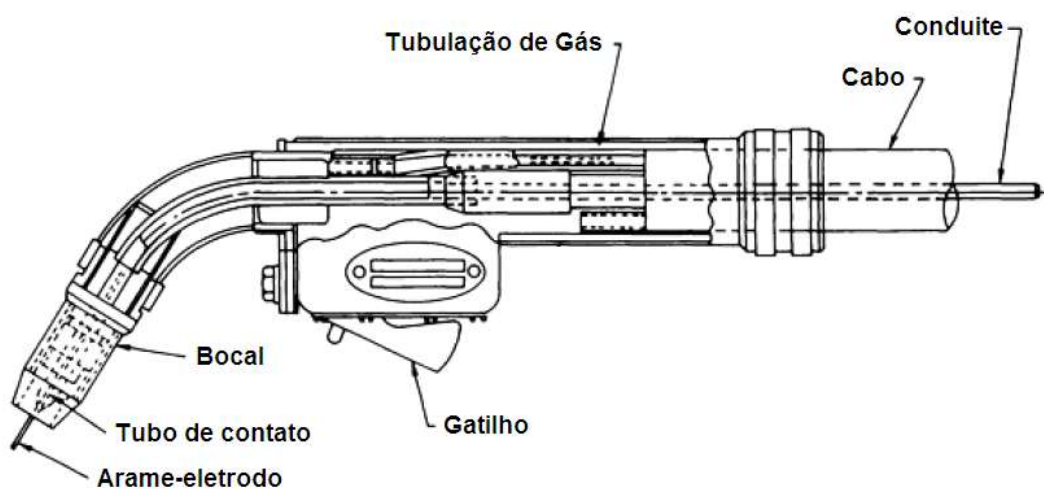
Tocha/pistola de soldagem utilizada para o processo MIG/MAG⁽³¹⁾.
